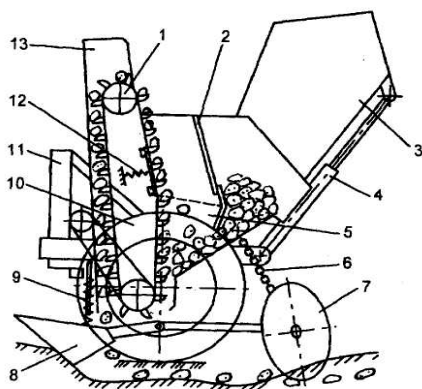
Схема рабочего процесса картофелесажалки Л-202: 1 – высаживающий аппарат; 2 – заслонка; 3 – загрузочный бункер; 4 – гидроцилиндр; 5 – питающий ковш; 6 – цепь; 7 – диски; 8 – сошник; 9 – штанга сошника с пружиной; 10 – опорно-приводное колесо; 11 – рама; 12 – вибратор; 13 – кожух
